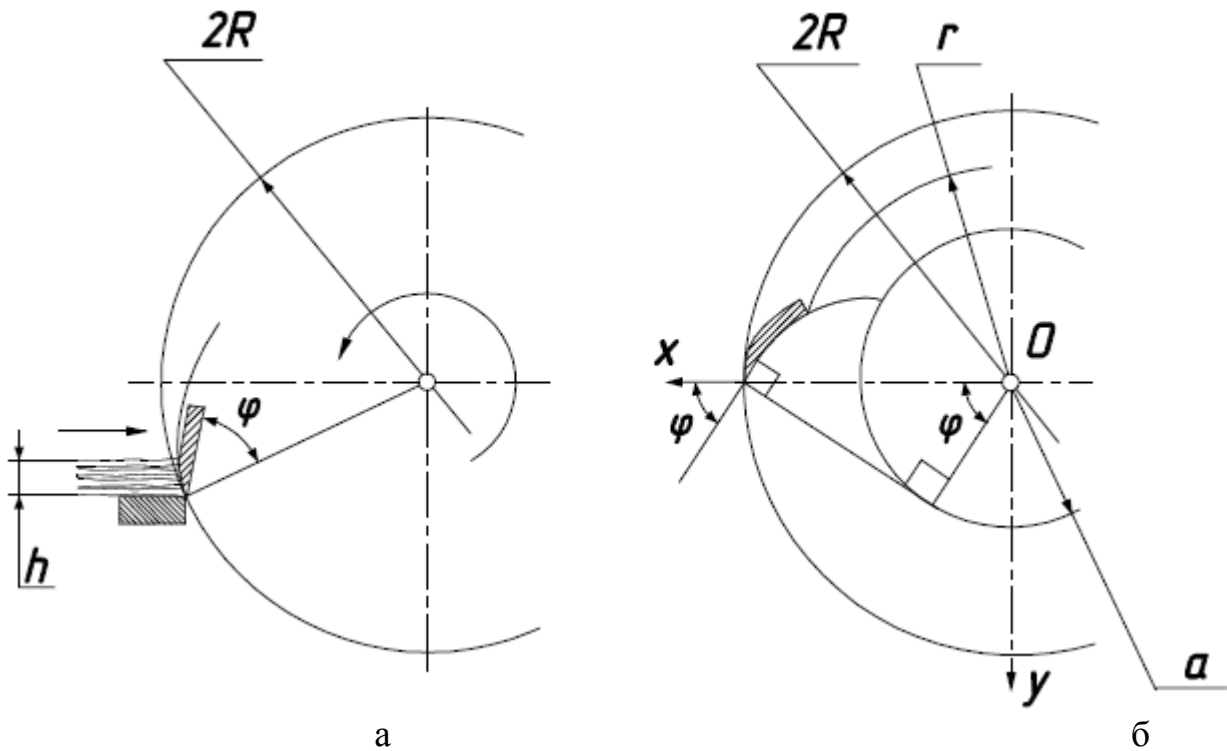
До конструювання поверхні гвинтоподібного ножа подрібнювального апарату барабанного типу:
